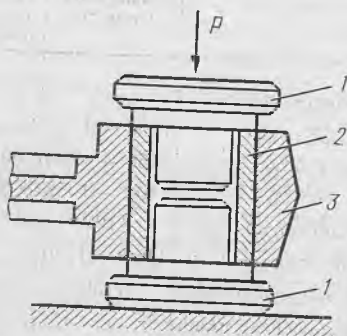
Восстановление втулок осадкой без выпрессовки
